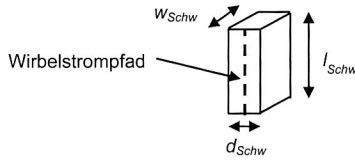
Schweißpaketierung, Maße des Verbinderwiderstands
